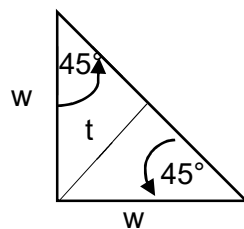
Dimensiones de la soldadura de filete en el mecanismo enfundador.
